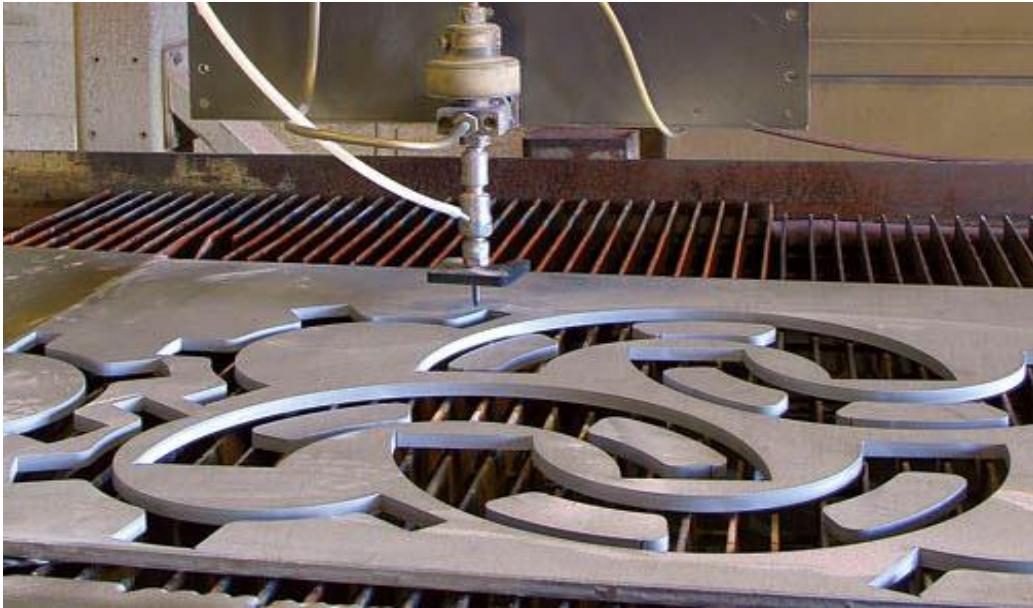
Lazer kesim makinası ile iki boyutta oluşturulup üç boyutlu hale getirilmiş olan strüktür çalışması
